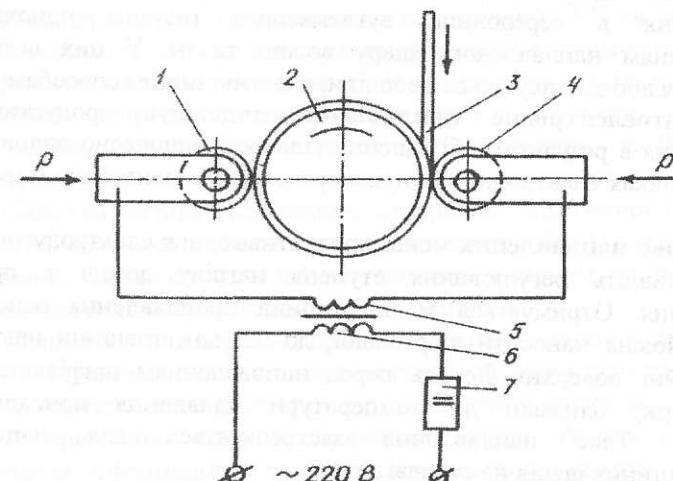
Схема електроконтактного наплавлення: 1,4 – контактний та наплавний ролик; 2 – деталь, що наплавляється; 3 – дріт, що наплавляється; 5 – вторинна обмотка трансформатора; 6 – первинна обмотка трансформатора; 7 – переривач
